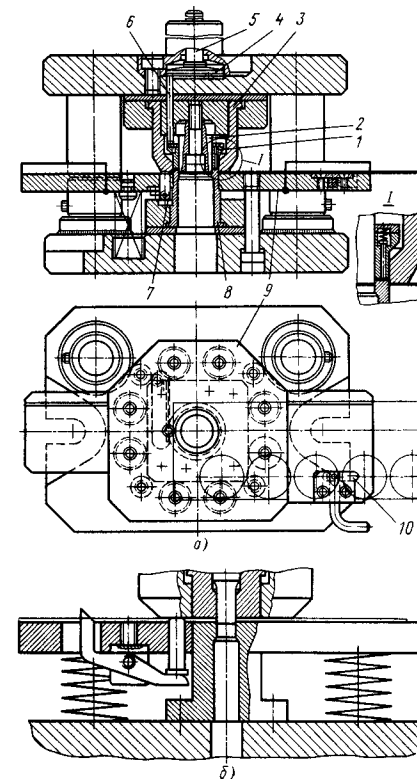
Конструкция штампа и автоматического упора при совмещенной вырубке—пробивке деталей
